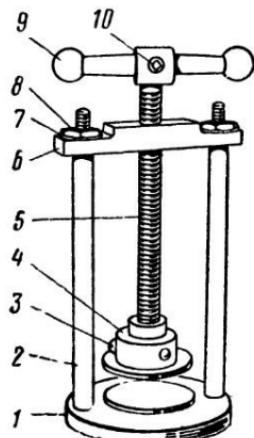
Винтовой пресс: 1 — основание; 2 — стойка; 3 — стопорный винт; 4 — пята; 5 — винт; 6 — попечерина; 7 — шайба; 8 — гайка; 9 — ручка; 10 — стопорный винт.
